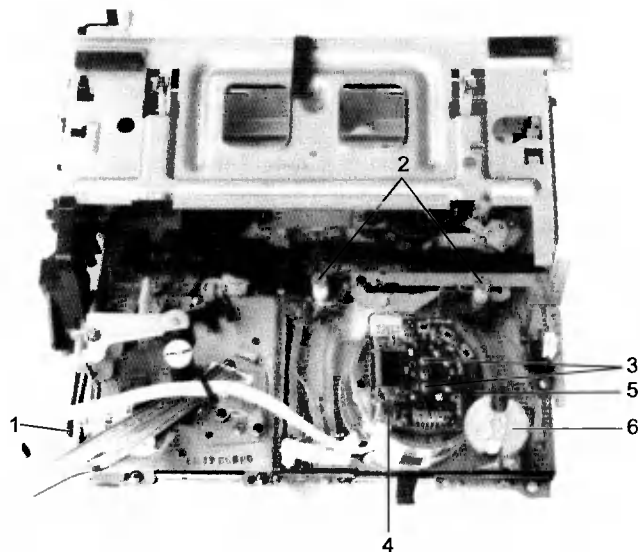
Внешний вид лентопротяжного механизма PMC0015A
